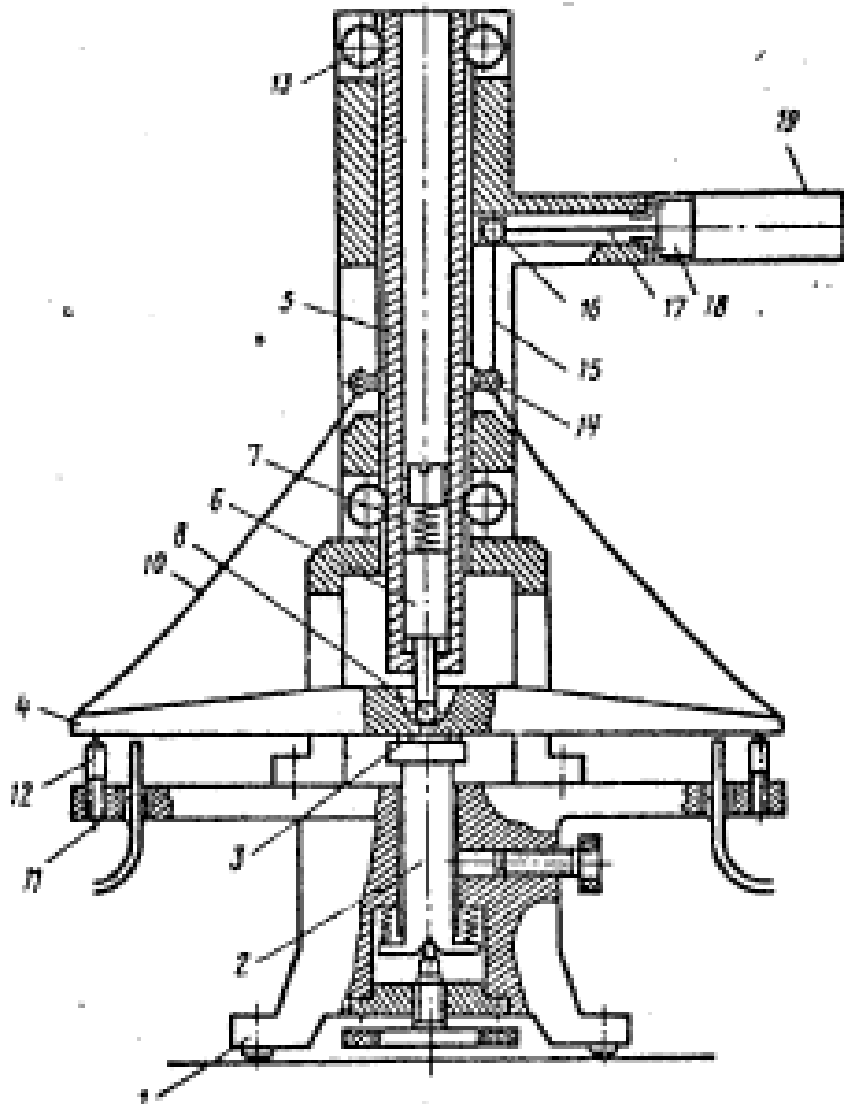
Пристрій для вимірювання непаралельності і товщини пластин
